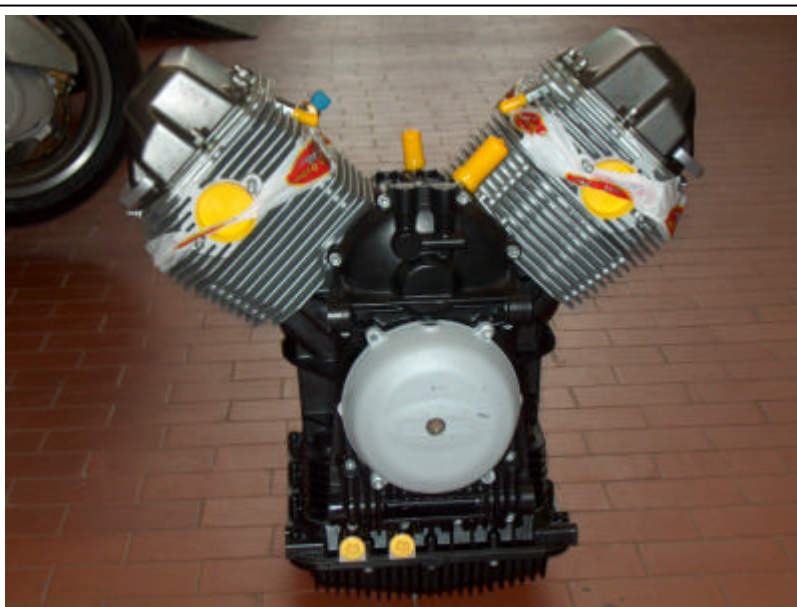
V11 : COUVERCLE ALTERNATEUR, BOUCHONS ECHAPPEM.
